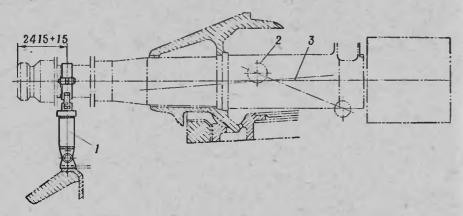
Схема установки прибора для проверки момента фрикциона: I- прибор для проверки момента фрикциона; 2- ось цапф; 3- ось трубы
